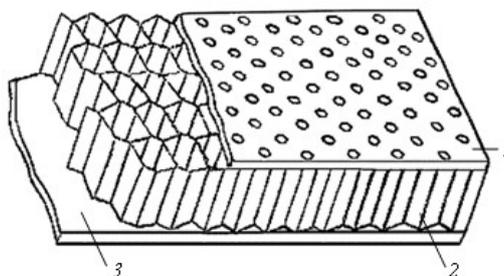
Схематичное изображение однослойной звукопоглощающей конструкции [5]:
